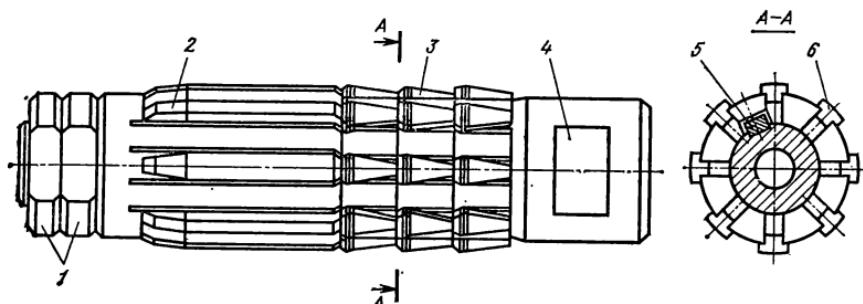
Прошивка шлицевая калибрующая с напаянными твердосплавными выглаживающими зубьями
